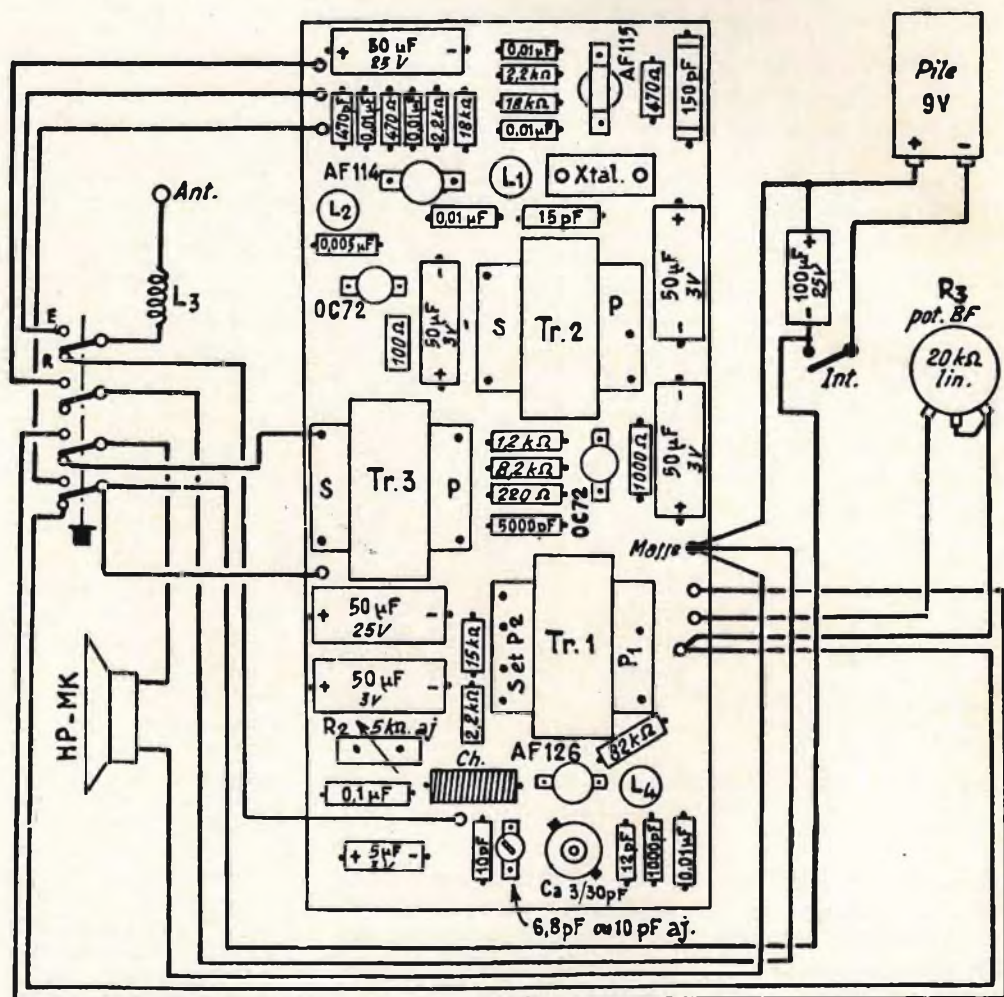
Schema di cablaggio del ricetrasmittitore a cinque transistori descritto in queste pagine.
